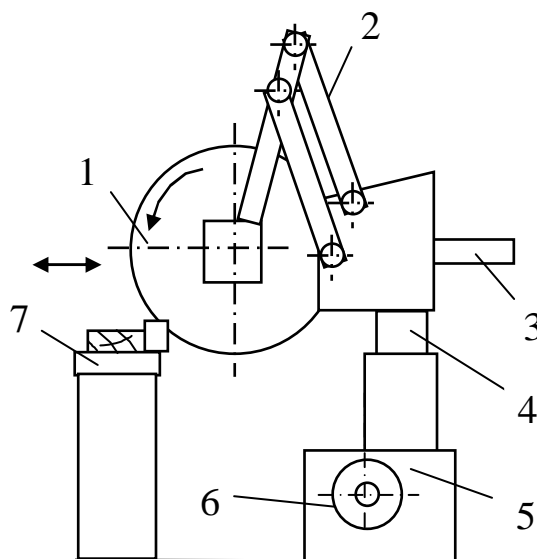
Схема рычажно-шарнирного торцовочного станка
